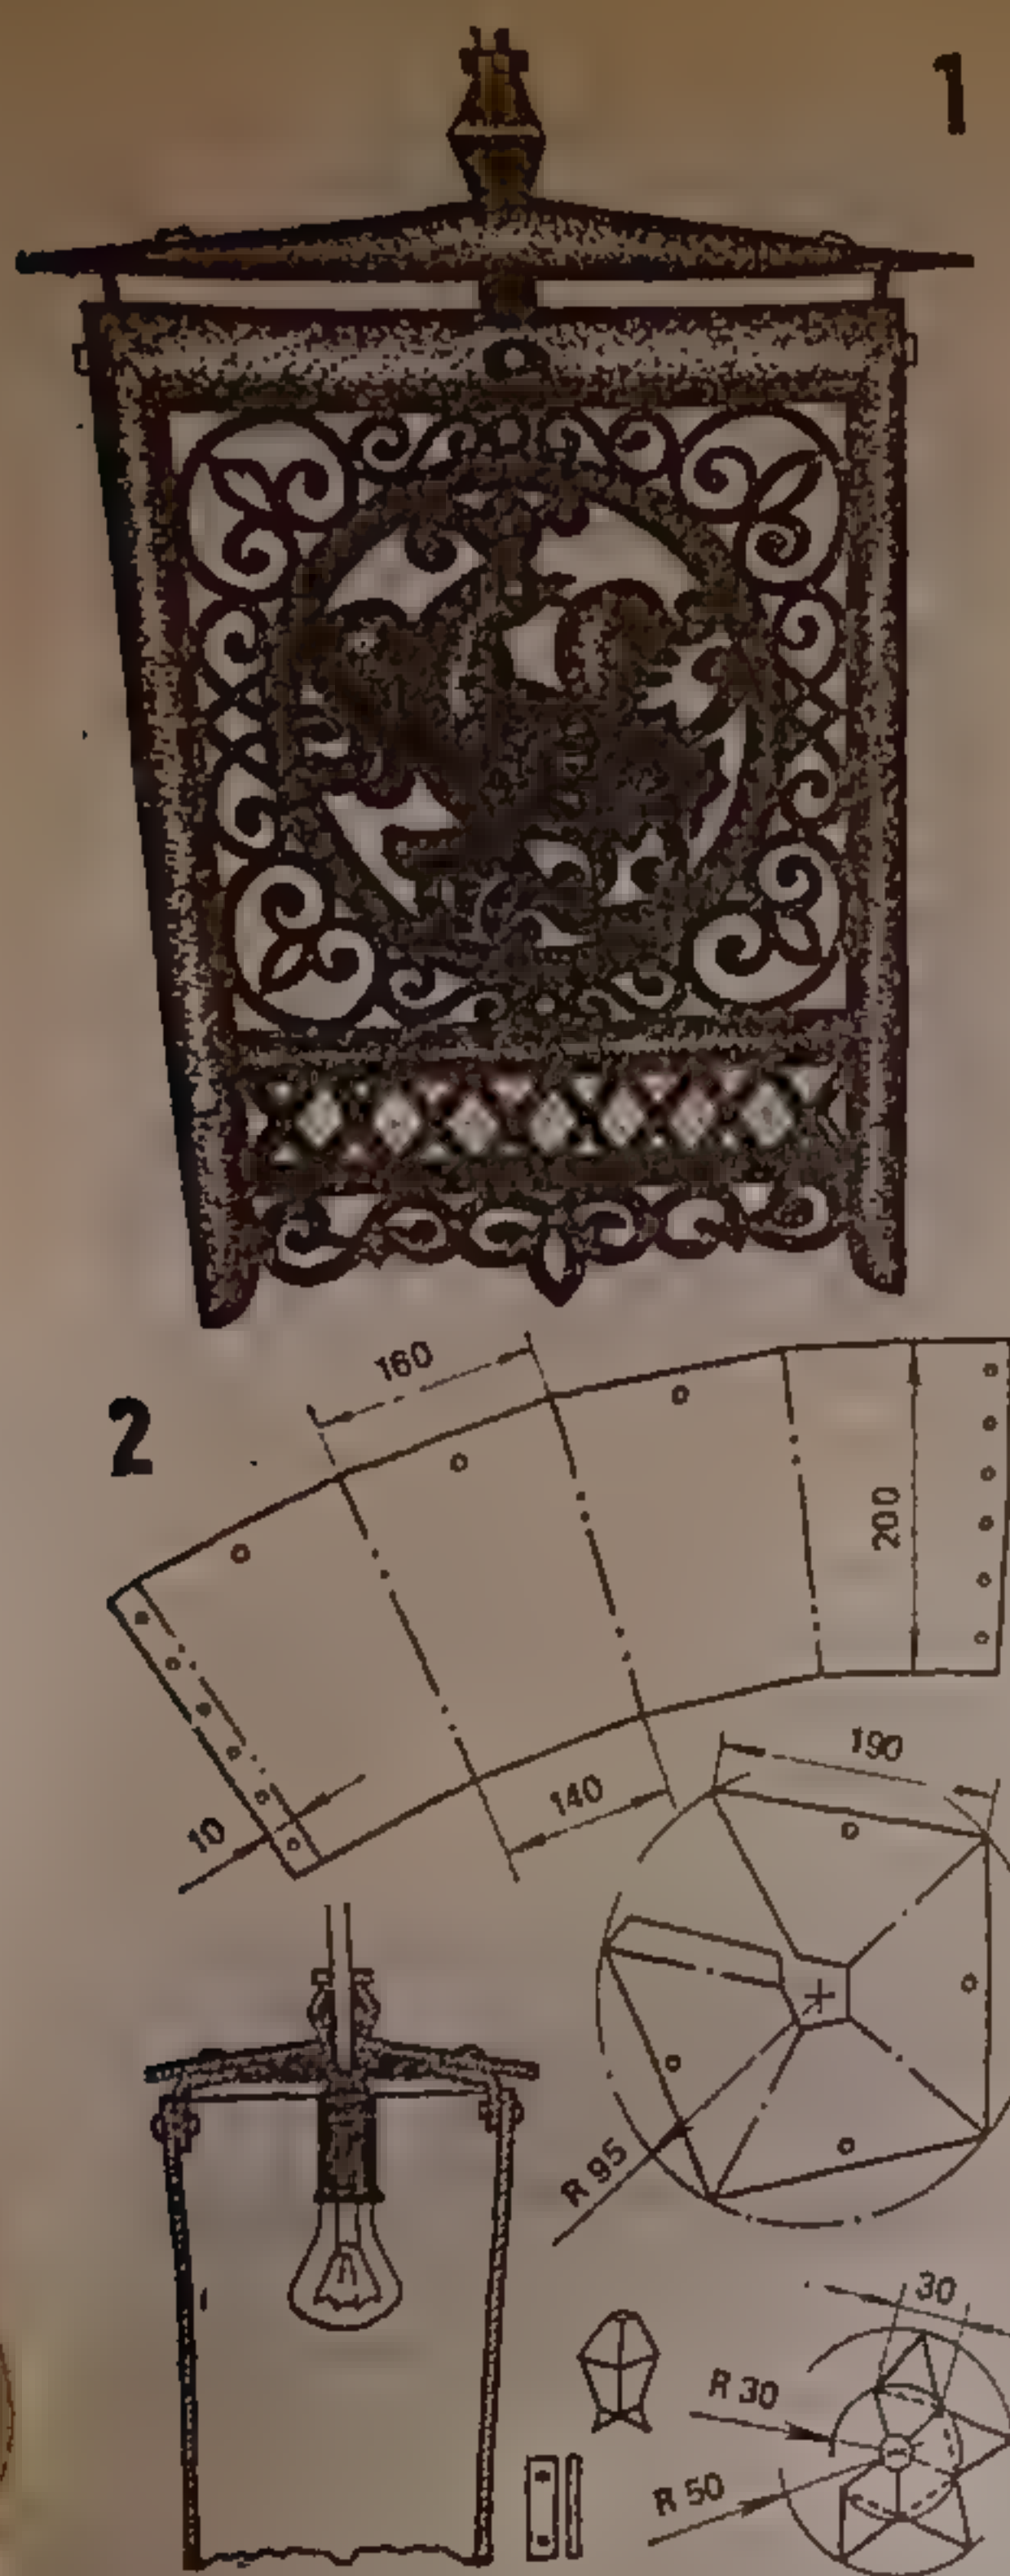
Фонарь из просечного металла: 1 — внешний вид; 2 — развертки деталей и сборочный чертеж
